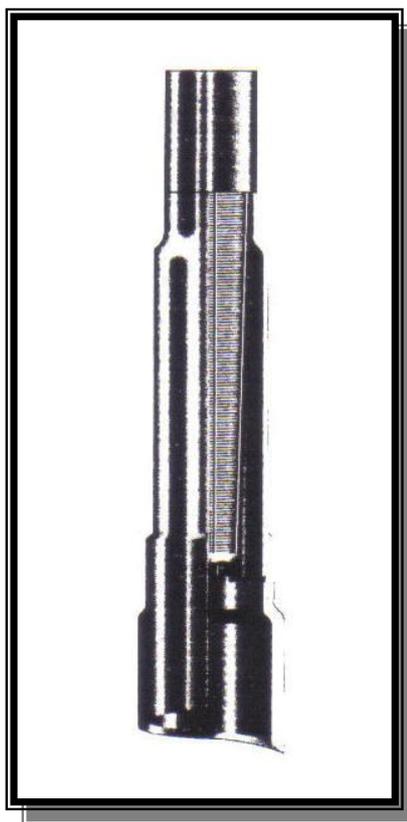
“Taper Tap” con camisa y guía, fuente: Bowen Fishing tools Technical Manual No.2800.
